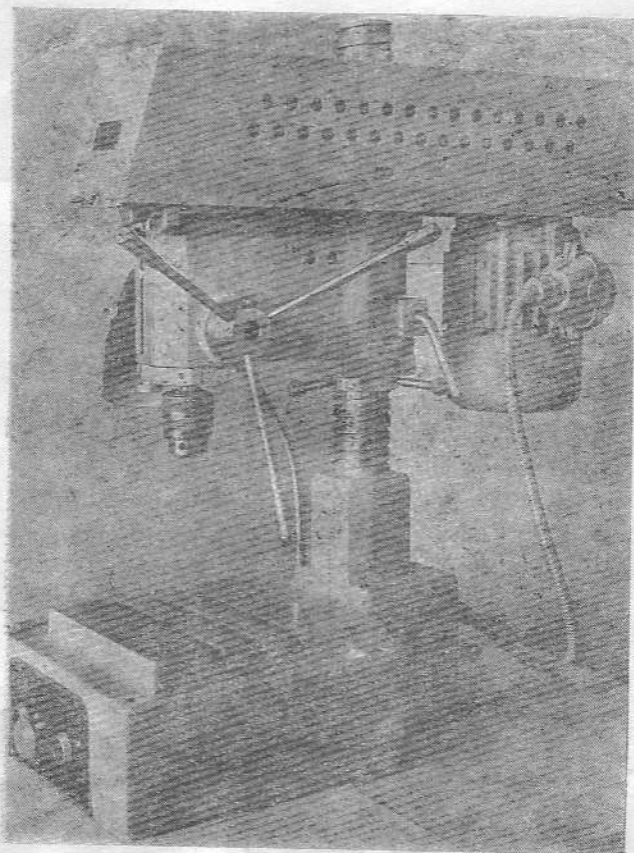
Станок настольно-сверлильный вертикальный модели 2М112
